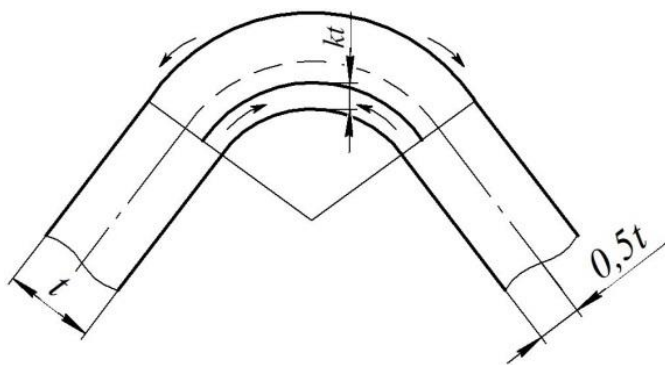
Теоретичне переміщення нейтральної вісі при згинанні заготовки
